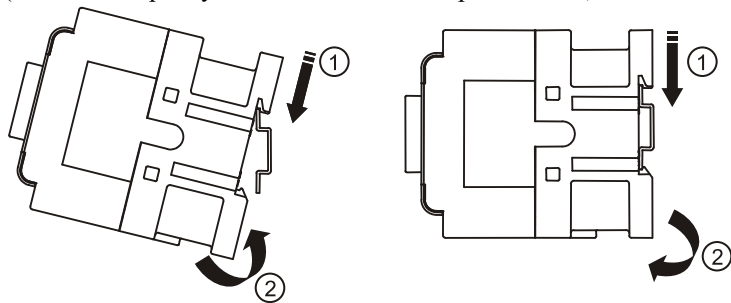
Способ установки /демонтажа контактора на токи 6-38А
